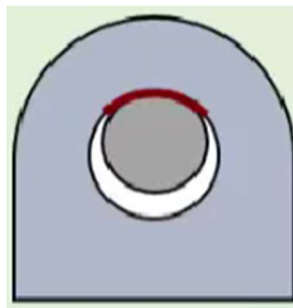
Falla de cizallamiento. (Engineering Solved, 2016)
